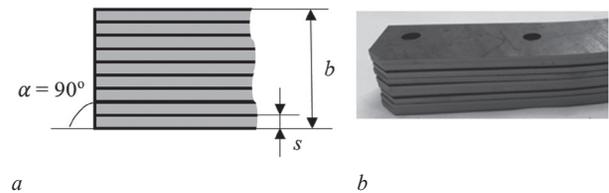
Схема расположения листовых выкроек в пакете (*a*) и внешний вид пакета листовых выкроек (*b*) (фрагменты)
